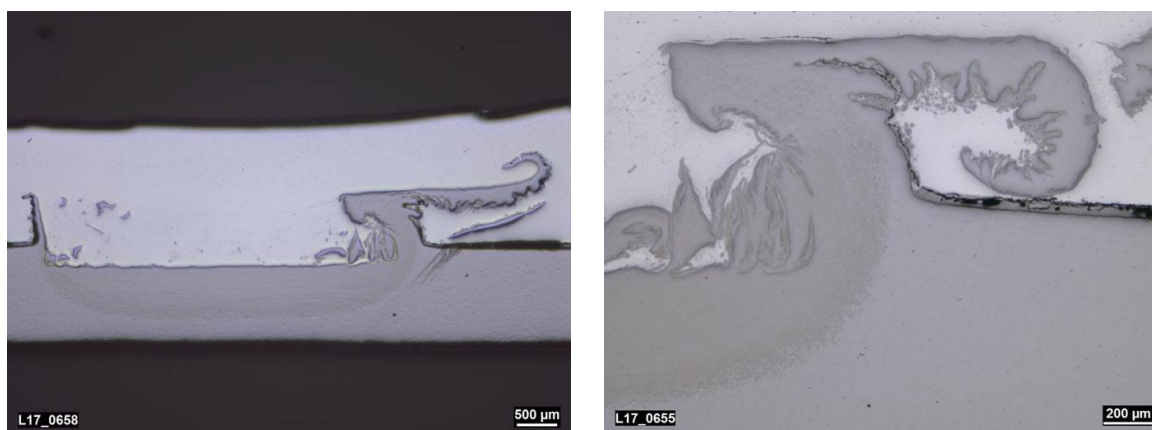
Schlibfbilder der Schweißung mit 22MnB5 und EN AW 6016 T4
